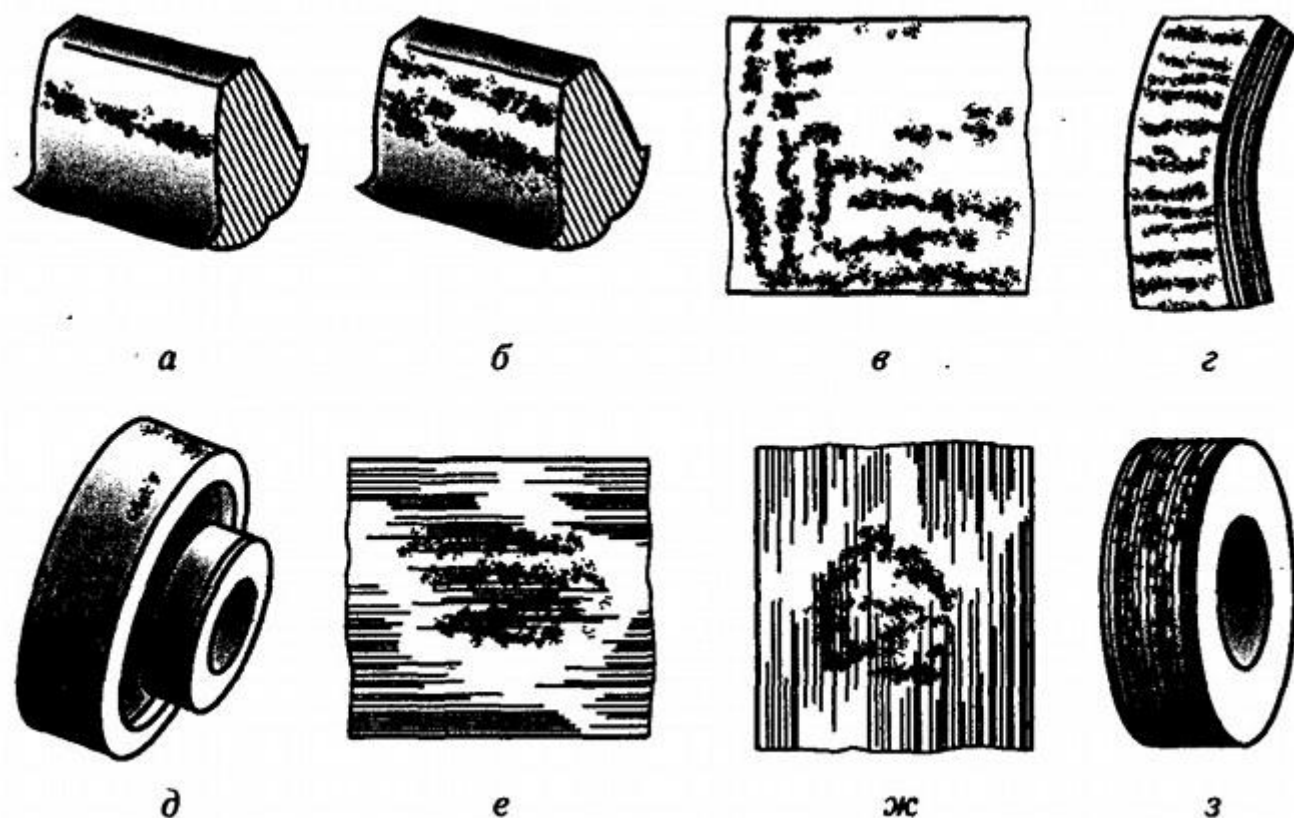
Характерные виды износа поверхностей скольжения: а — выкрашивание; б — отслаивание; в — коррозия; г — эрозия; д — царапины; е — задиры; ж — налипание; з — глубокий вырыв материала и перенос его с другой поверхности трения
